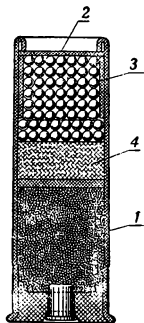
Дробовой патрон, снаряженный папковым кольцом для улучшения кучности боя стволов цилиндрической сверловки: 1 — гильза, 2 — дробовой пыж, 3 — бумажное кольцо (концентратор), 4 — пороховой пыж
